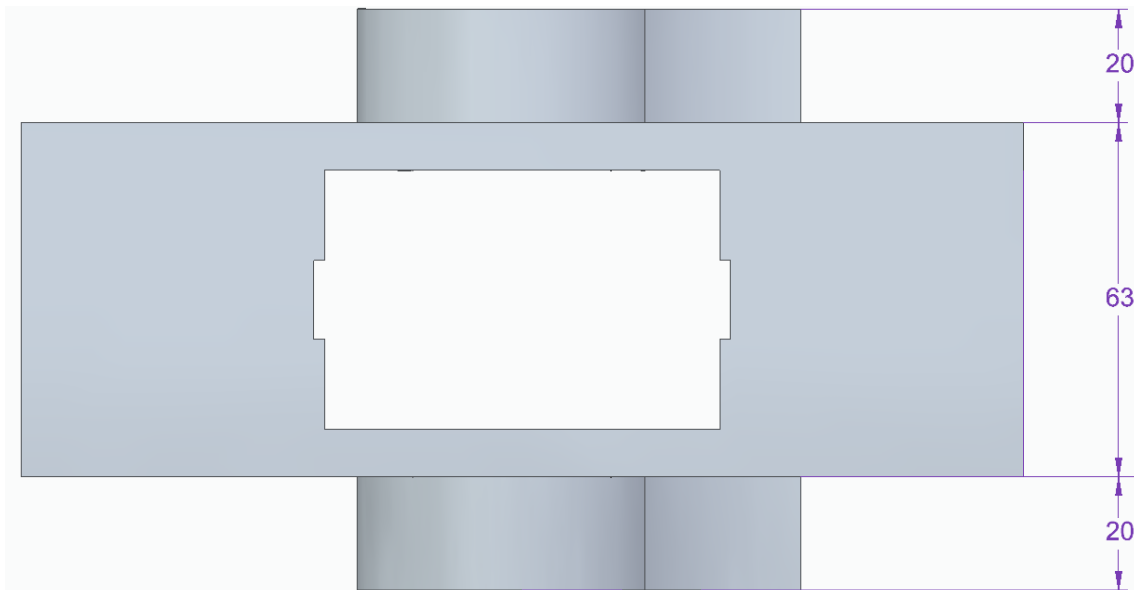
Planta de la pieza base 2. Fuente: elaboración propia
